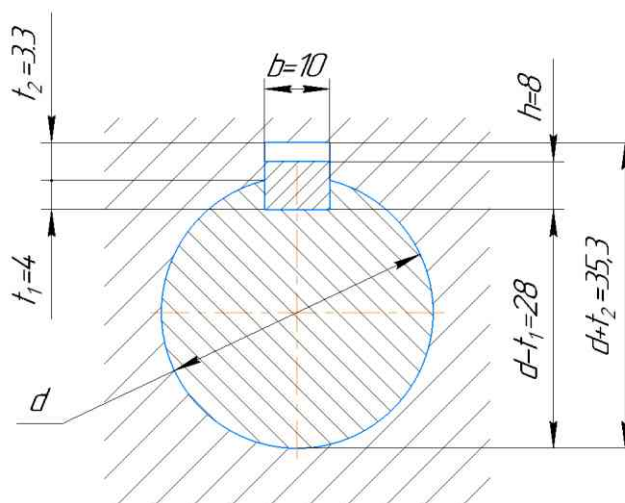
Схема шпонкового з'єднання фрези фасонної циліндричної [11]
